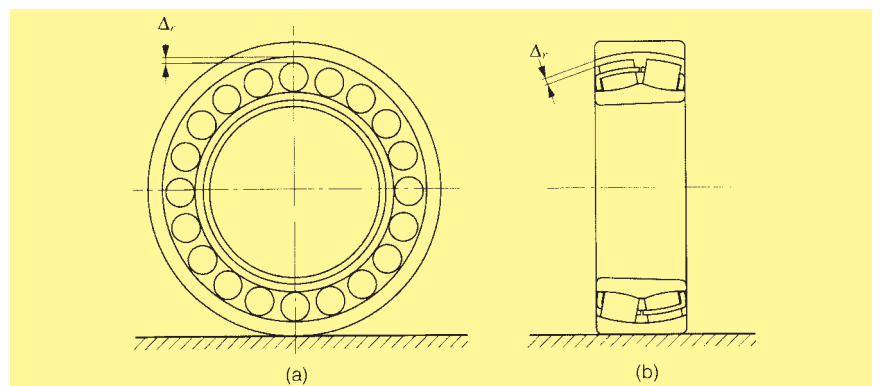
Medição de Folga no Rolamento Autocompensador de Rolos
